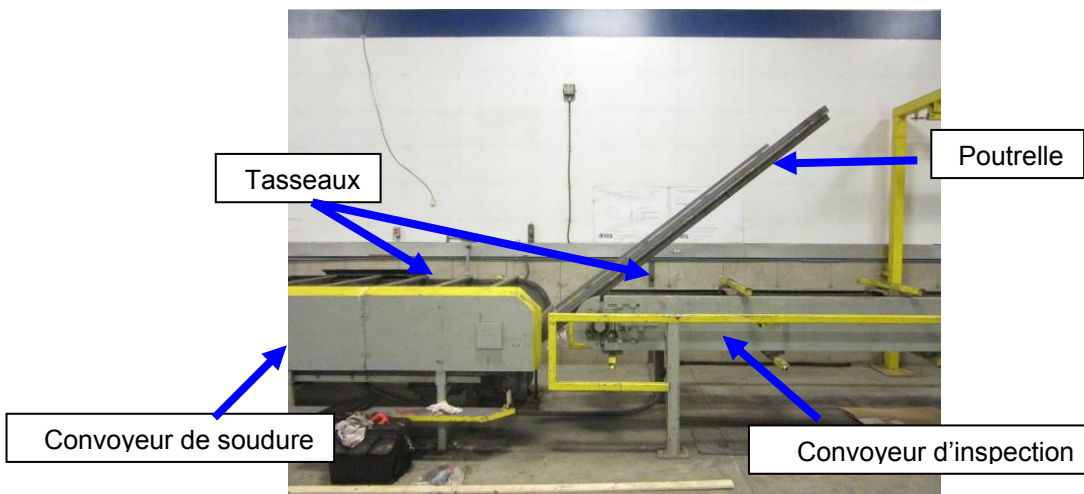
Poutrelle en appui sur les tasseaux du convoyeur de soudure et du convoyeur d'inspection
